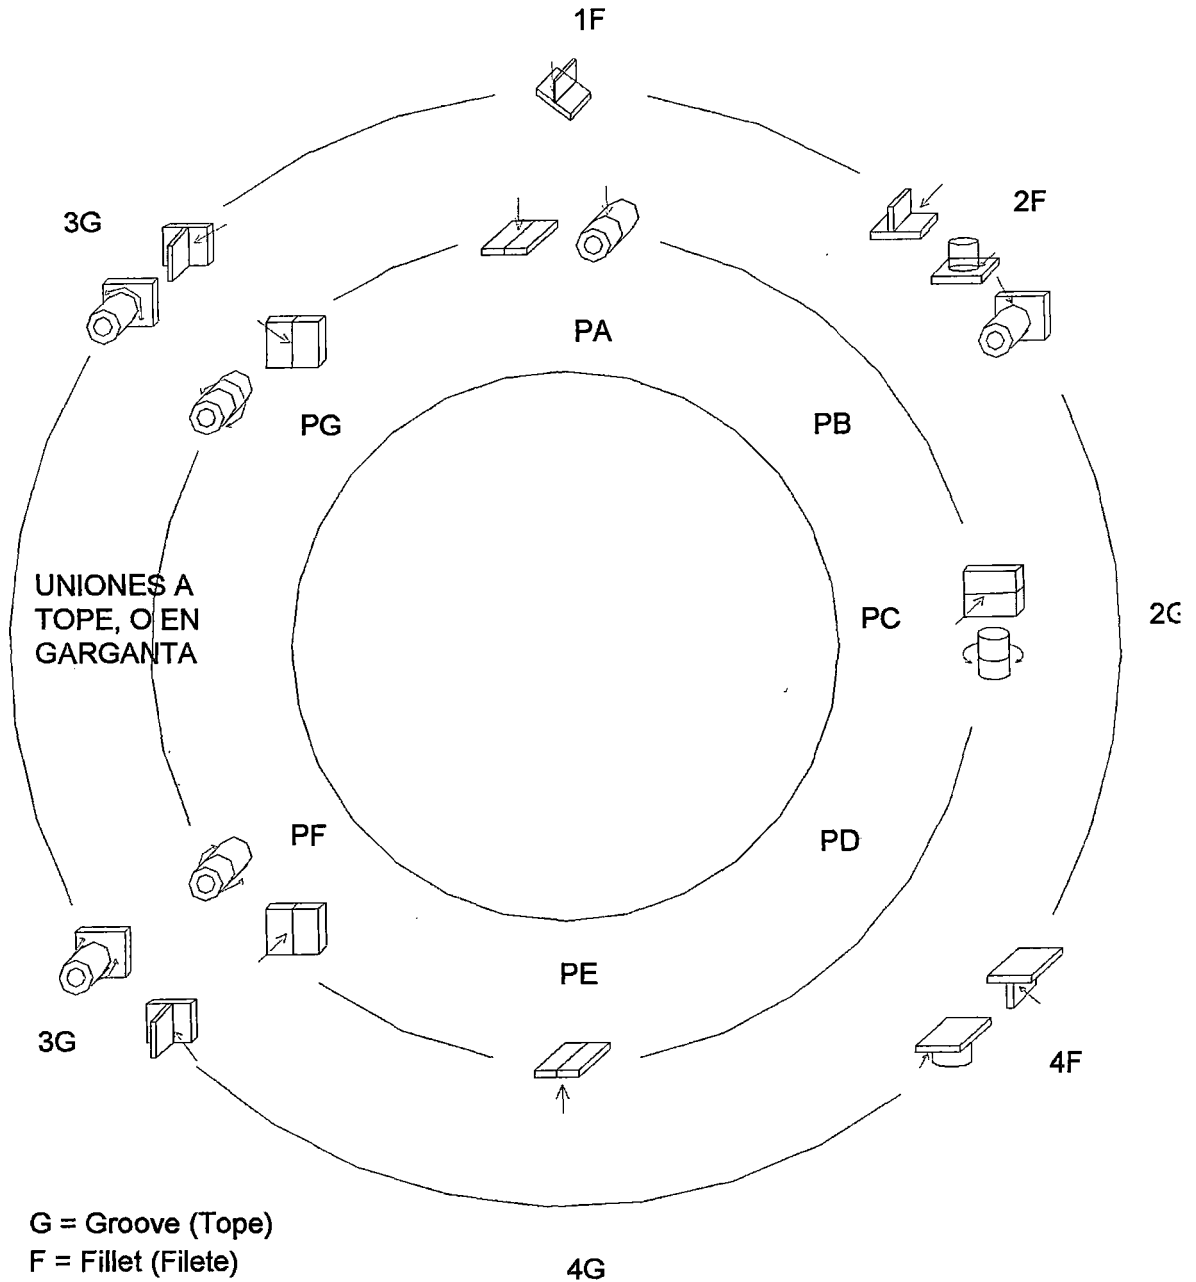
Posiciones de Soldadura según norma DIN 6947
